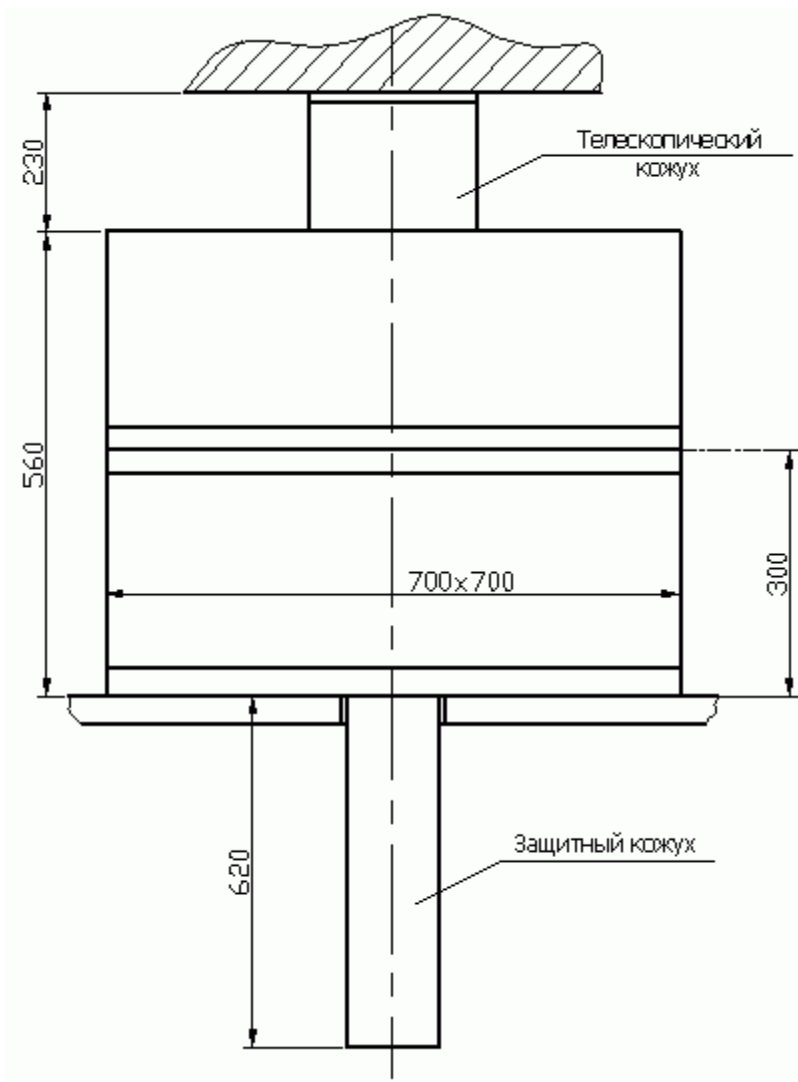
Установка коническо-винтового редуктора на телах качения
